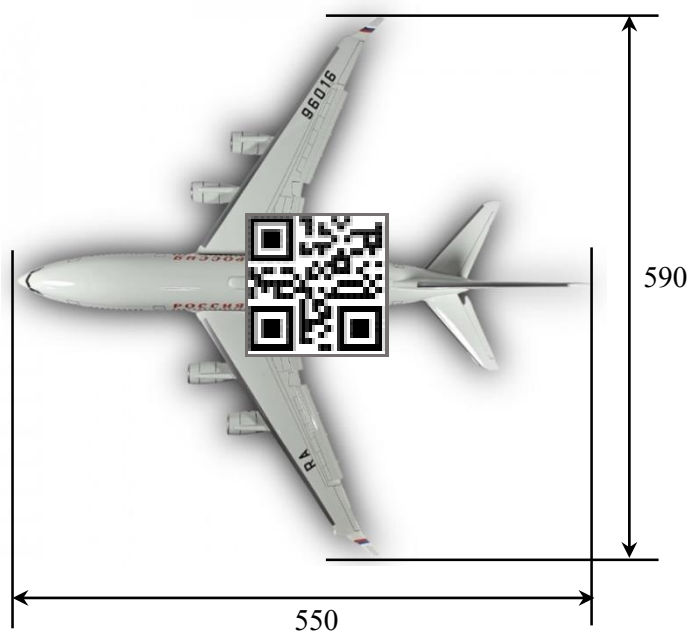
Чертёж самолета с площадкой для QR-кода (вид сверху)
